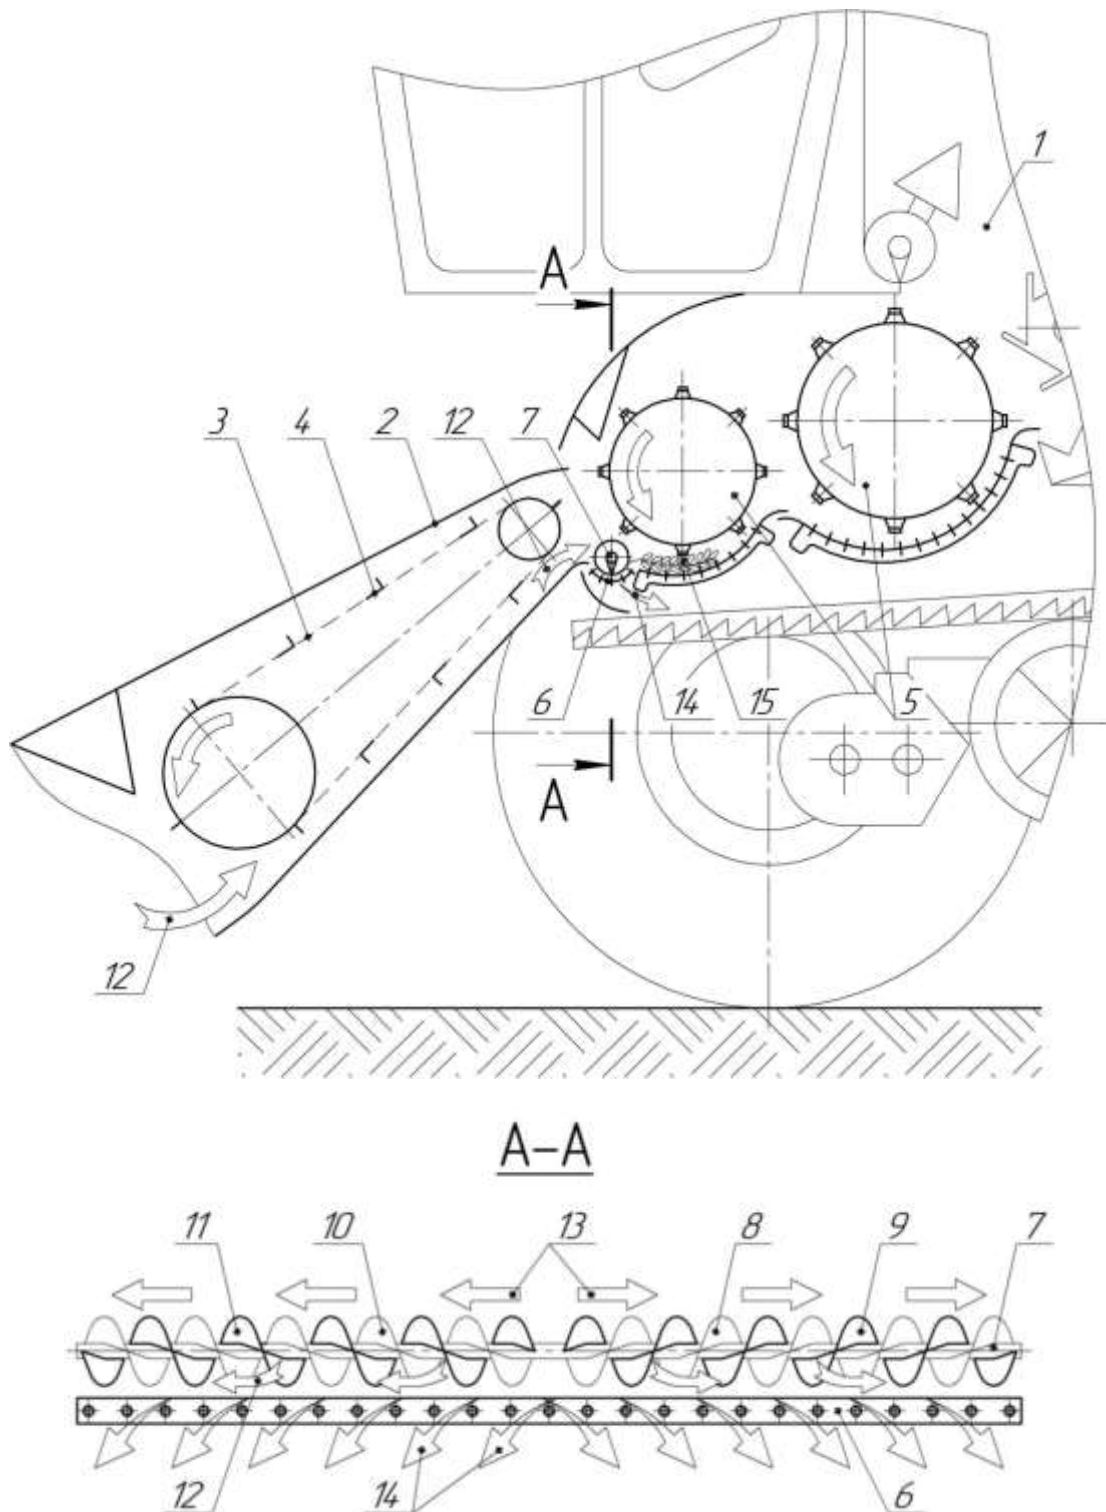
Зерноуборочный комбайн, снабженный устройством для предварительного выделения свободного зерна (Патент РФ № 2658389): 1 – комбайн; 2 – наклонная камера; 3 – транспортер; 4 – скребок; 5 – молотилка; 6 – сепарирующая решетка; 7 – шнек; 8-11 – витки шнека; 12 – хлебная масса; 13 – направление движения хлебной массы; 14 – свободное зерно; 15 – колосовая часть урожая
